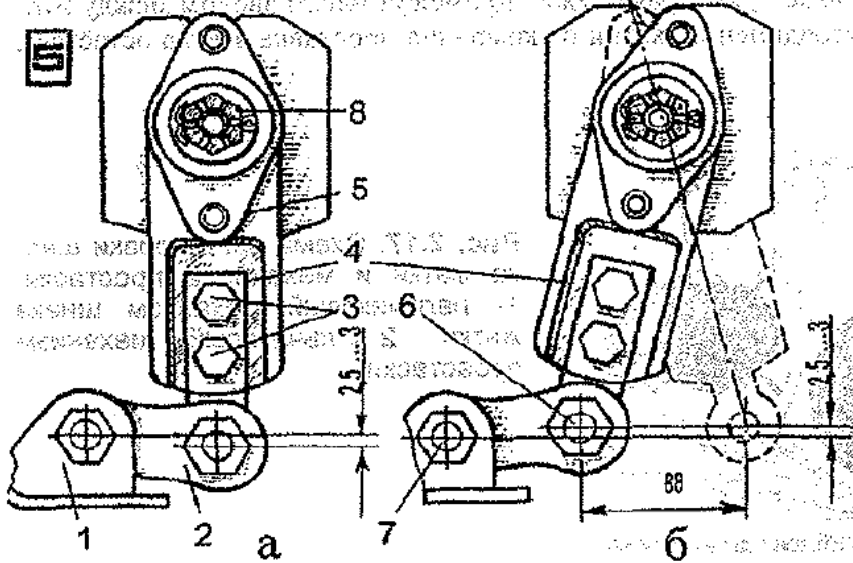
Схема регулировки привода ножа: 1 – головка ножа; 2 – щетка; 3 – болты; 4 – головка рычага; 5 – рычаг; 6 – ось шарнира головки рычага; 7 – ось шарнира головки ножа; 8-гайка
